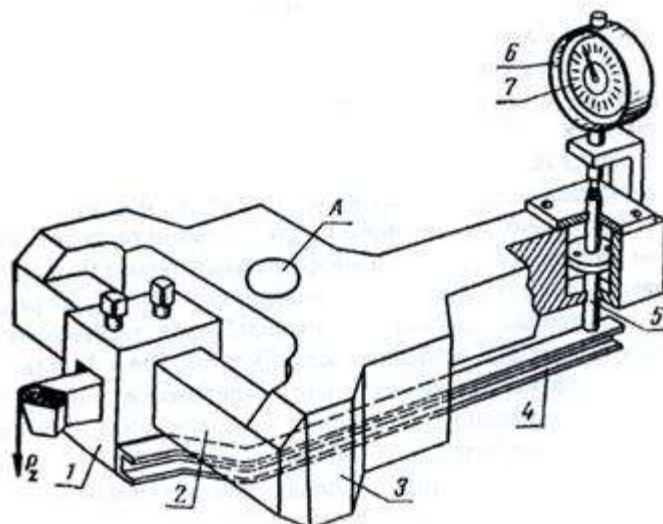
Однокомпонентный динамометр механического типа ДК-1
